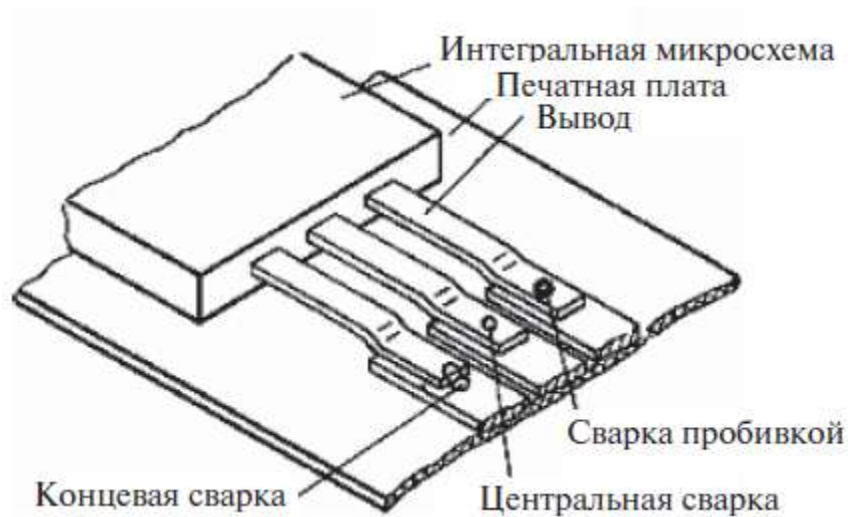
Разновидности монтажной лазерной сварки
